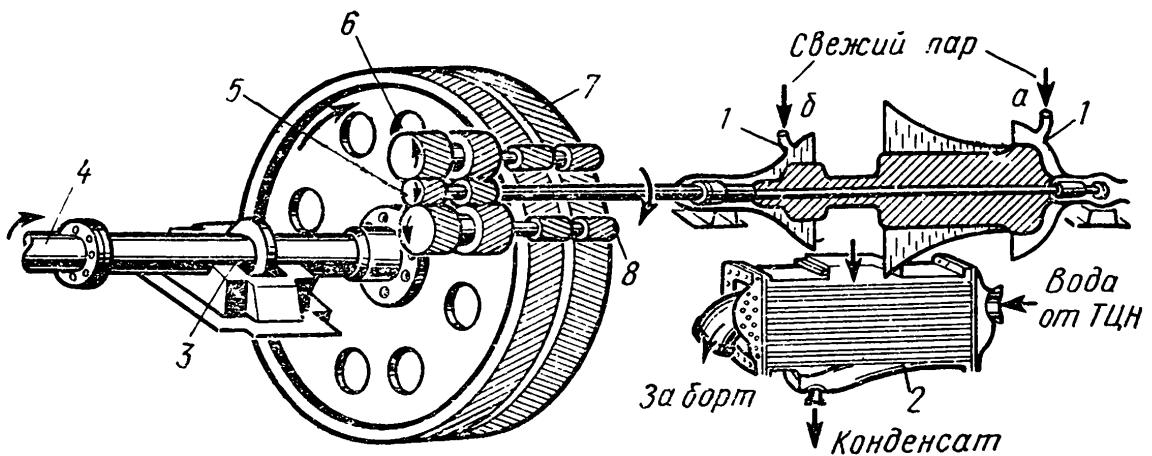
Схема двухступенчатого зубчатого редуктора паровой турбины:
